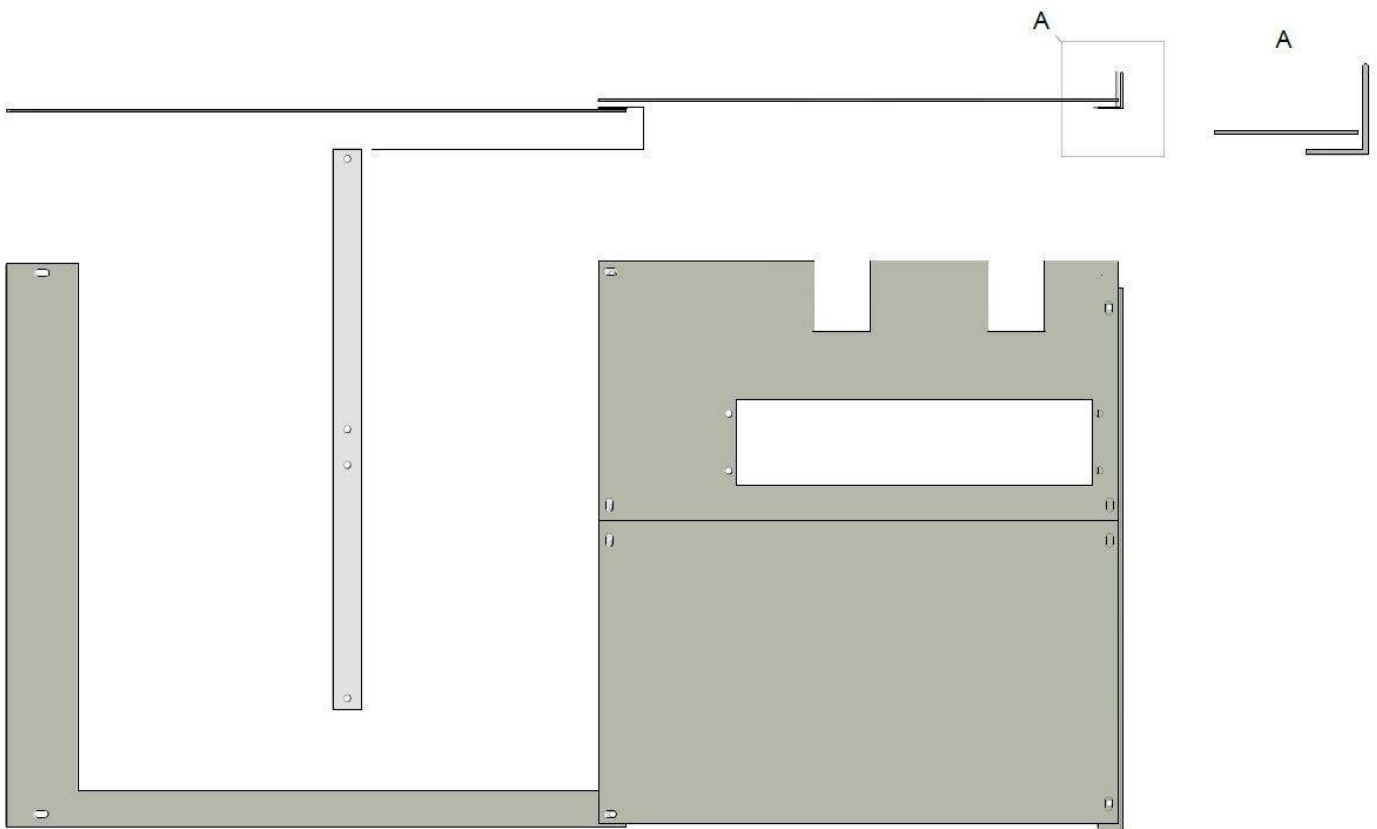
planimetria e particolare della sezione del piano in corrispondenza del QBT
